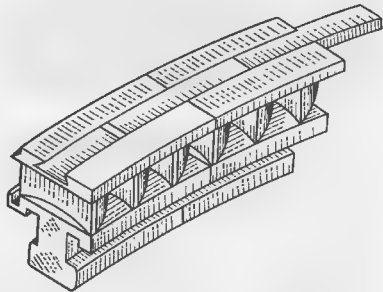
Пакеты рабочих лопаток с демпферной связью для регулирующей ступени ЦВД
